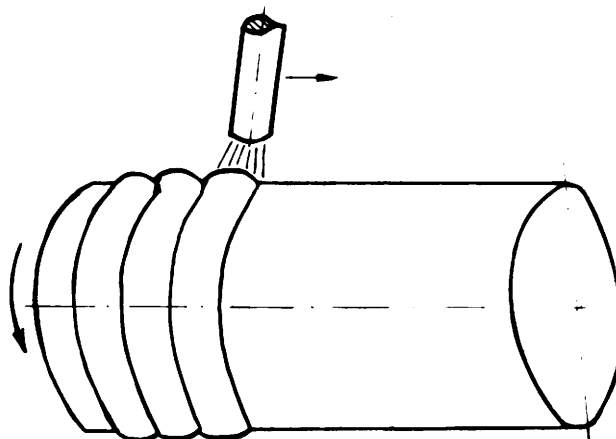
Наплавка цилиндрических поверхностей по винтовой линии
